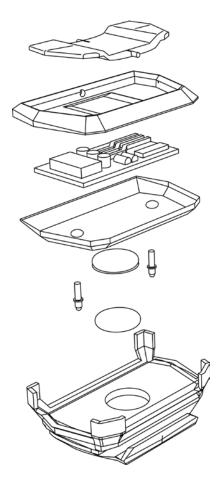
Sistema manubrio. Fuente: López, Otero (2016)
